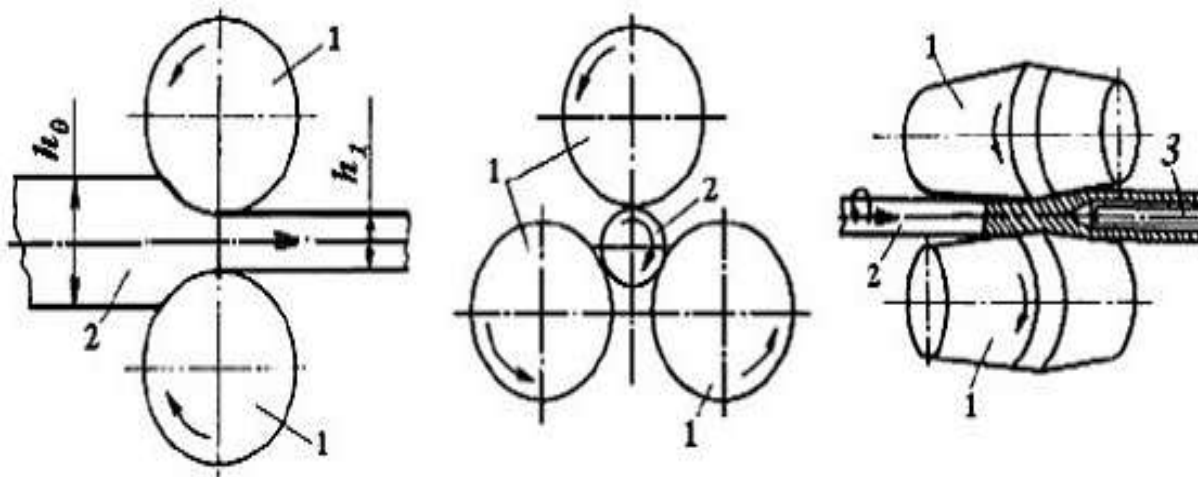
Схеми основних видів прокатки: а – повздовжня; б – поперечна; в – поперечно-гвинтова; 1 – валки; 2 – заготовка; 3 – оправлення
